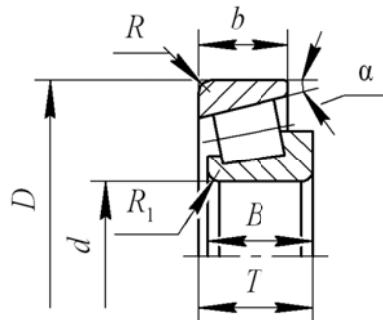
Габаритные размеры роликовых конических однорядных подшипников
